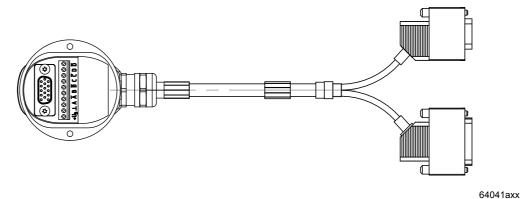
Anschlussdeckel mit zwei Sub-D (1 × 9-polig und 1 × 15-polig)
